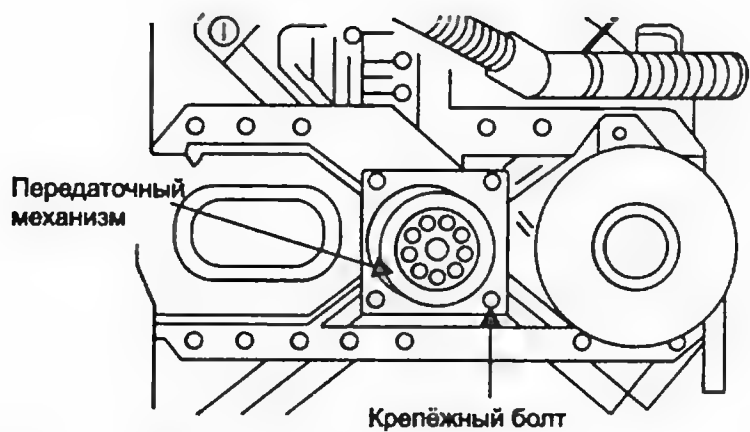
Демонтаж механизма передачи (редуктора)
